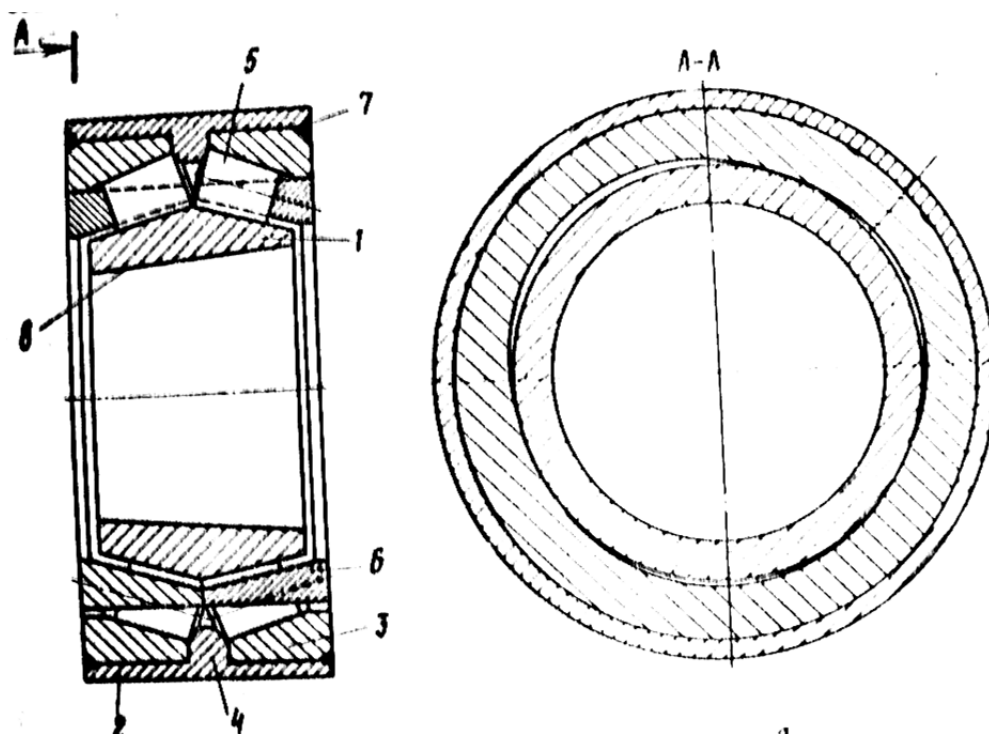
Роликовий сферичний дворядний підшипник
